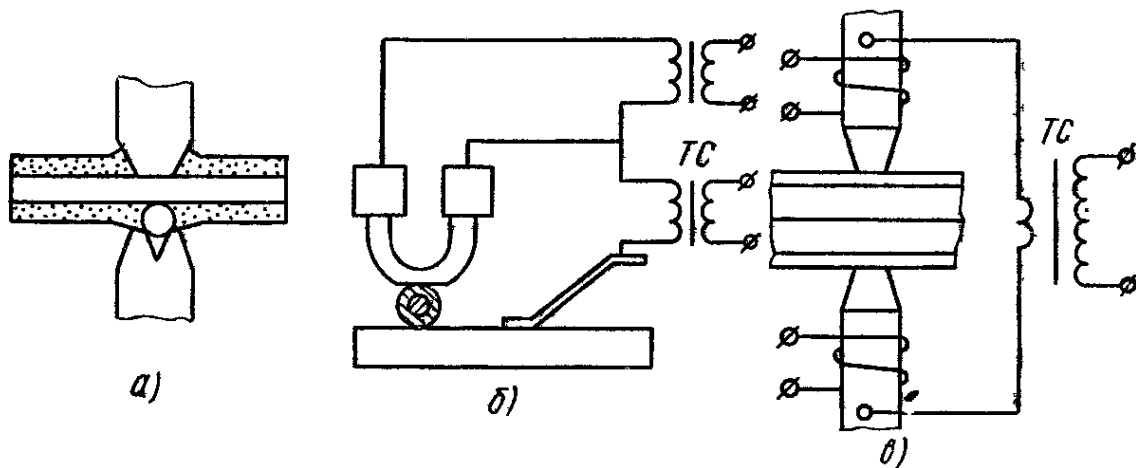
Способы создания металлического контакта при сварке деталей с пластмассовым покрытием:
